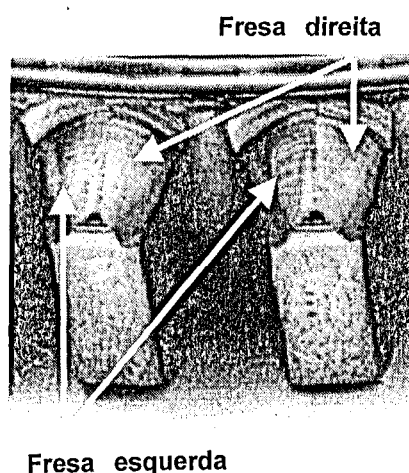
Perfil dos dentes da engrenagem usinado pela fresa direita e fresa esquerda.
